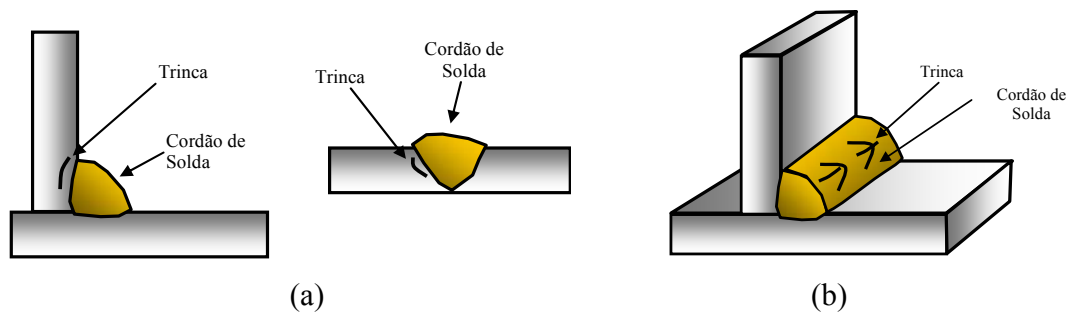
Formação de Trincas Nas Juntas Soldadas: (a) À Frio; (b) À Quente
